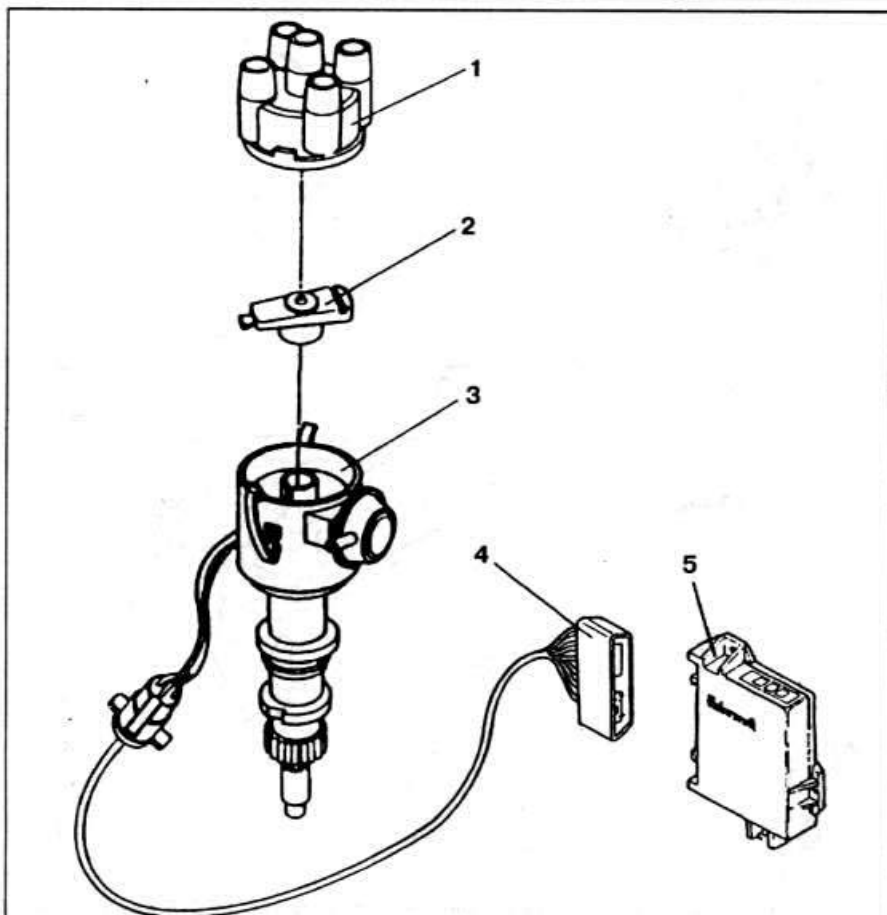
Детали распределителя зажигания двигателей «REC» и «NEL»:
